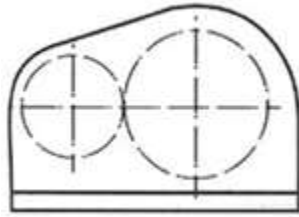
Схема цилиндрического одноступенчатого вертикального редуктора.
